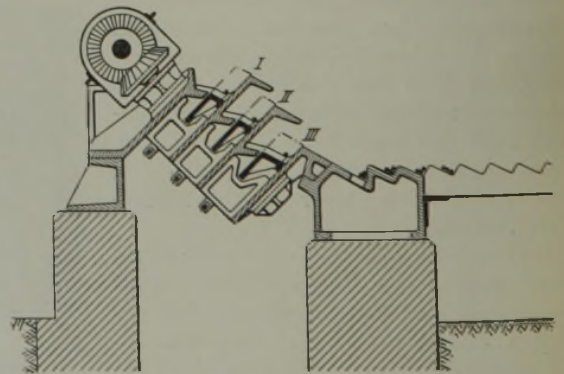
Kühlbett mit Aushebevorrichtung für drei Walzadern.
